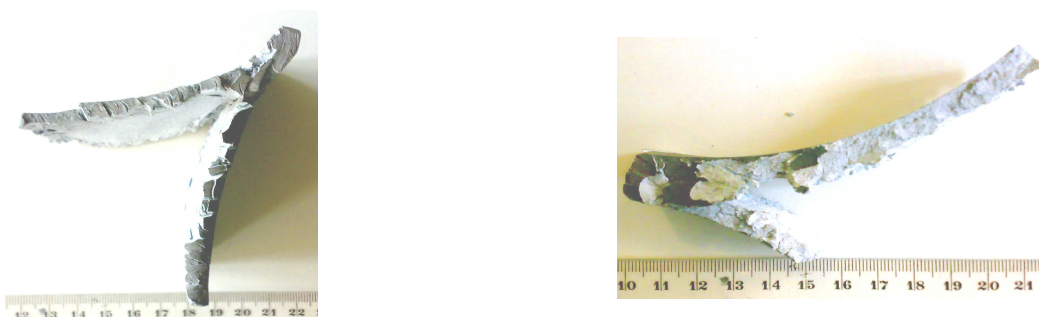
Вид разрушенных образцов в процессе прокатки
